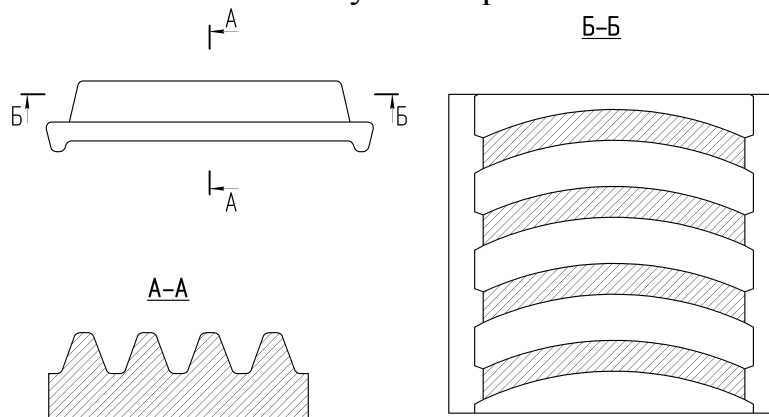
Зубчатая рейка с арочным зацеплением Новикова
